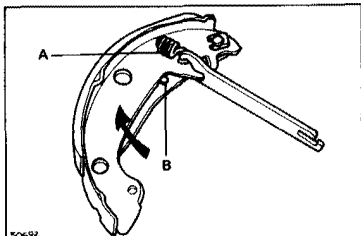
Пружина распорной планки — тормоза типа Bendix
